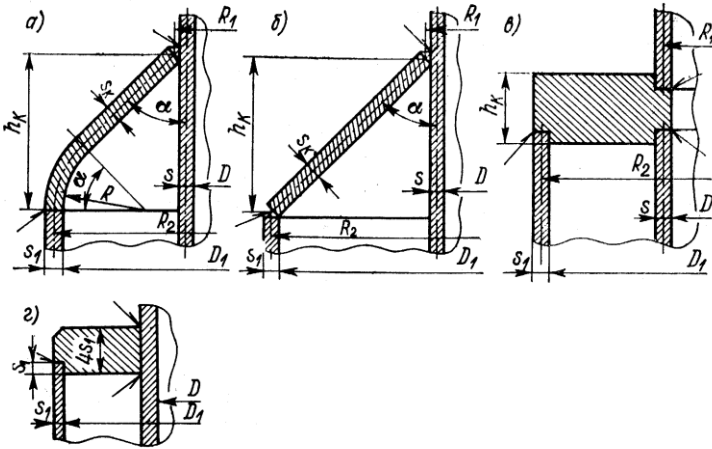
Конструкции соединительных элементов неразъёмных рубашек с корпусом аппарата: а – тороконическое; б – коническое; в – кольцевое; г – конструктивное соединение рубашки с корпусом аппарата
